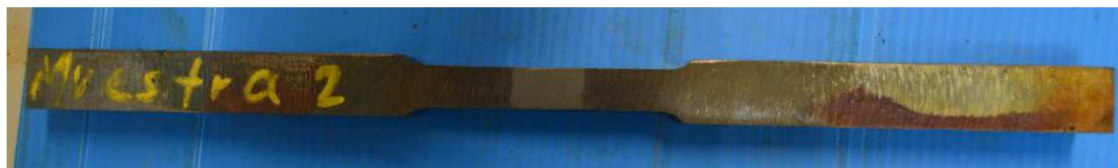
11 Fotografía de la probeta maquinada de la soldadura con cara de raíz de 3 mm
